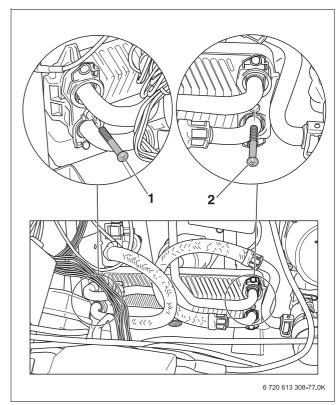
Schrauben vom Plattenwärmetauscher entfer-
